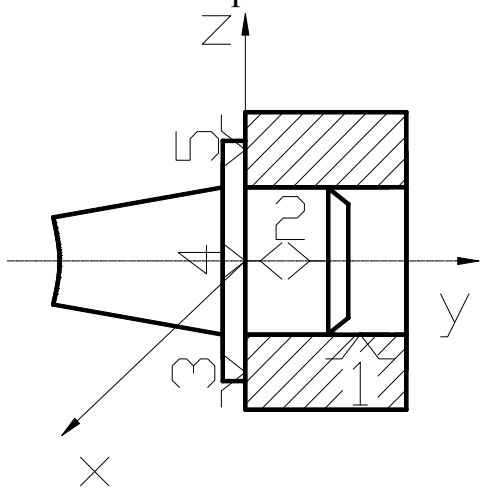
Базування по короткій внутрішній поверхні обертання (з зазором)
